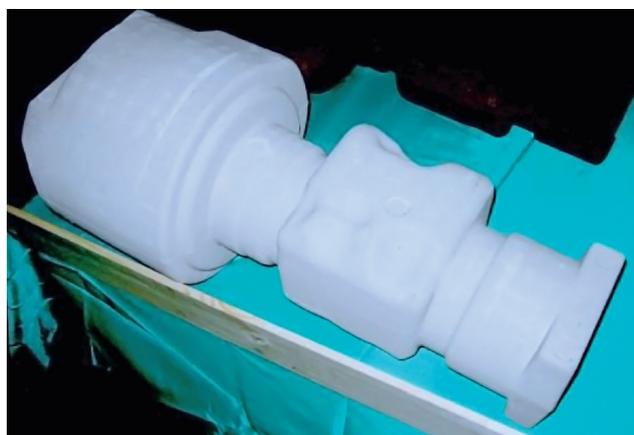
Цельный стержень отливки «рукав полуоси», изготовленный по Амин-процессу
